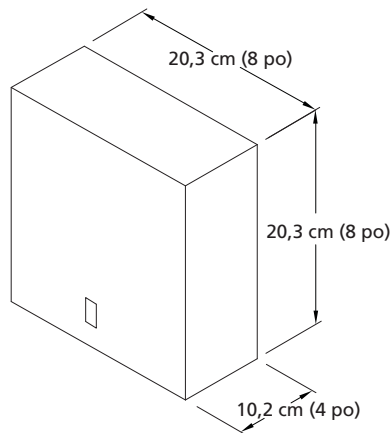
Dimensions du dispositif de verrouillage (6KWL7 & 6KWL8)
